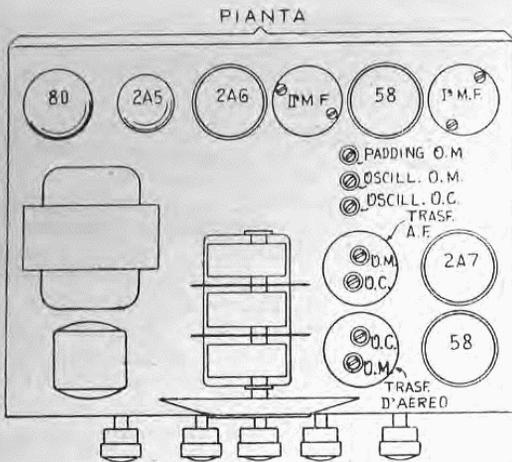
Posizione dei compensatori di A.F. e di M.F. (Trimmers) nella Super G-61.
